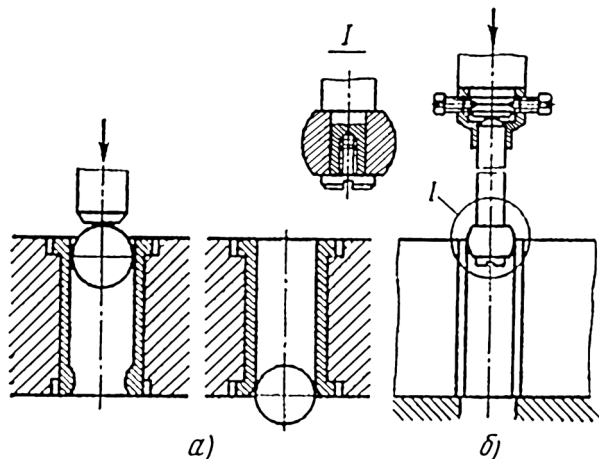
Калибровка подшипников-втулок после запрессовки:
